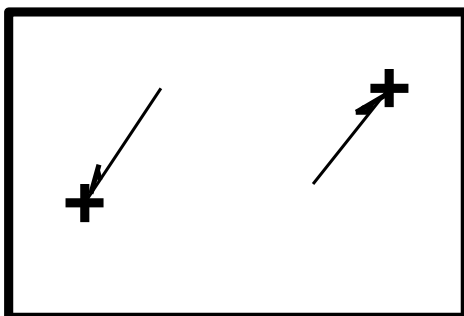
Изображение видимой одиночной сварной точки
